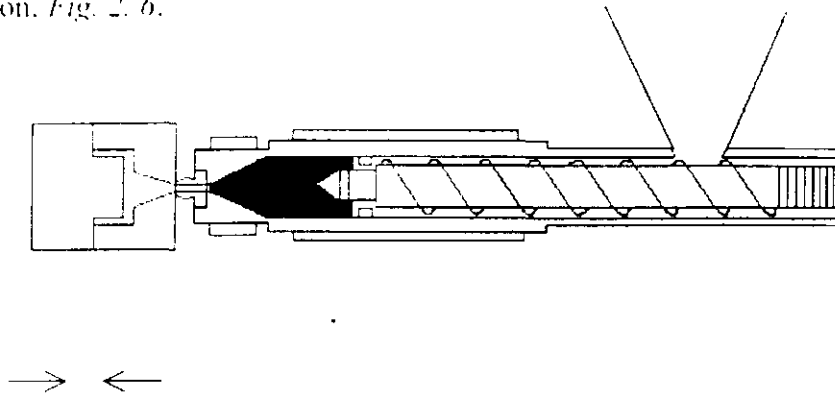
6 Cierre del molde e inicio de la inyección.
